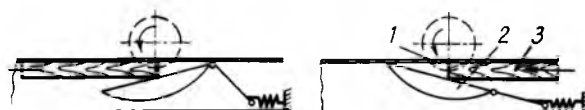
Схема выборки паза под сливной брусок: 1 — режущий инструмент; 2 — ограждение; 3 — деталь
